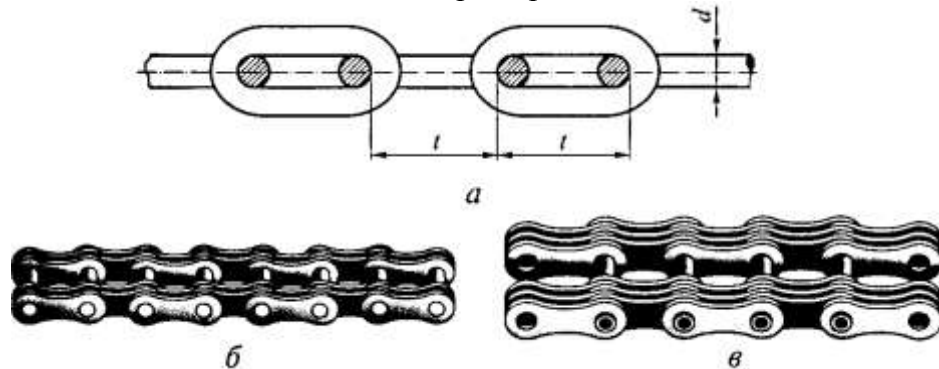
Сварные (а) и штампованные (б, в) цепи: d — диаметр проволоки цепи; t — шаг звена цепи
